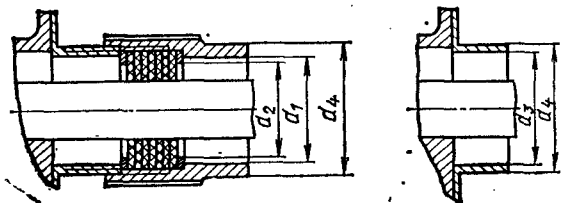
Подключение кабеля с резиновой или пластиковой оболочкой для двигателей с  $h=280-355$  мм.
